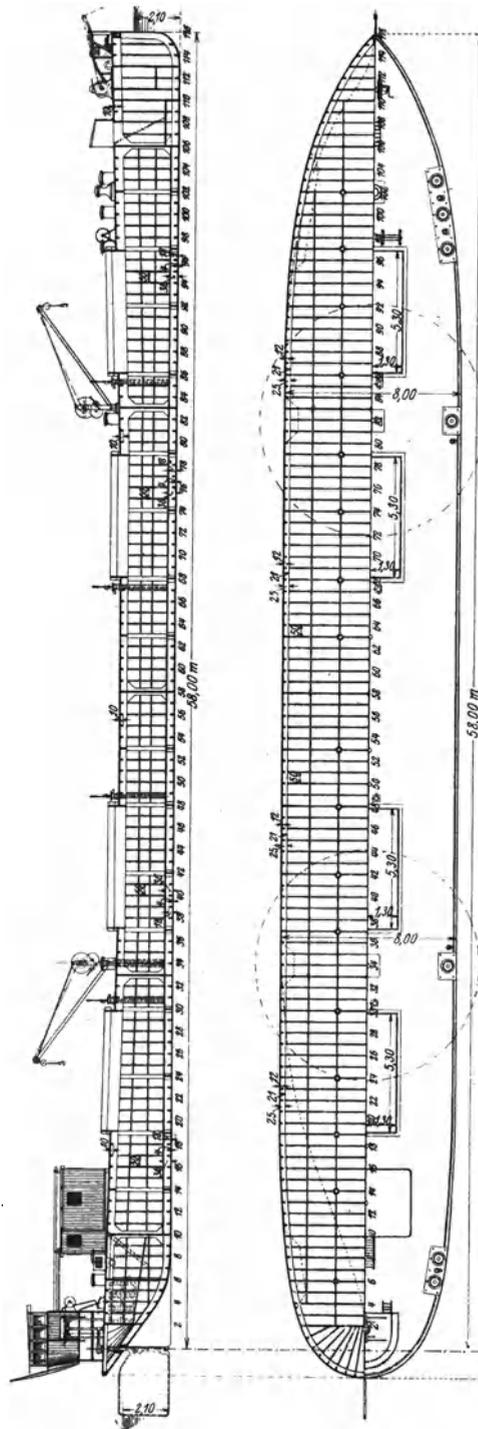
Donauschleppkahn, 700 t Tragt., Längsschnitt und Grundriß.
